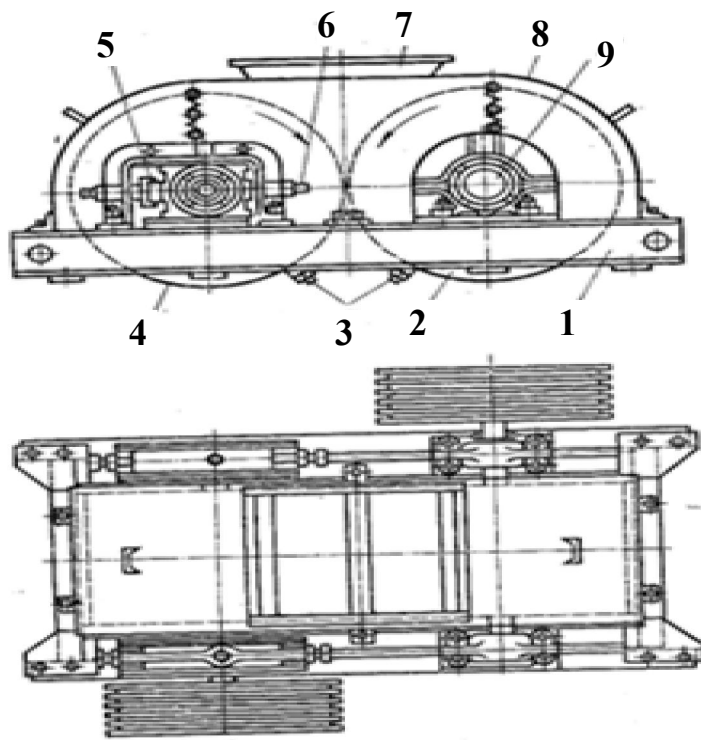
Диференційні вальці тонкого перемелювання: 1 – рама; 2 – нерухомий валок; 3 – скребки; 4 – рухомий валок; 5 – амортизатор; 6 – регулювальний гвинт; 7 – завантажувальна лійка; 8 – кожух; 9 – підшипникові опори
